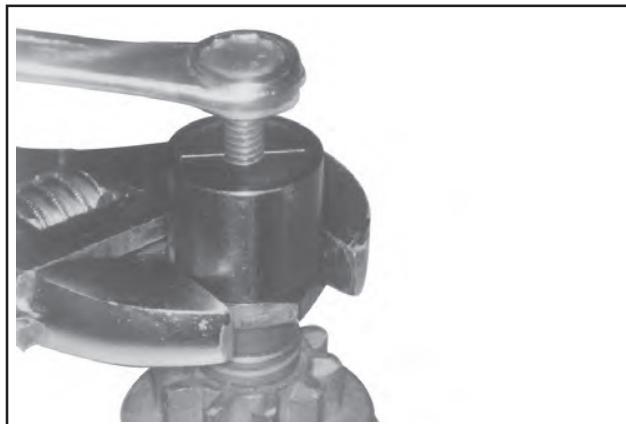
Dichtung des Werkzeugs und Drehung der mittleren Schraube (Uhrzeigersinn) für die Entfernung des Halterings.
